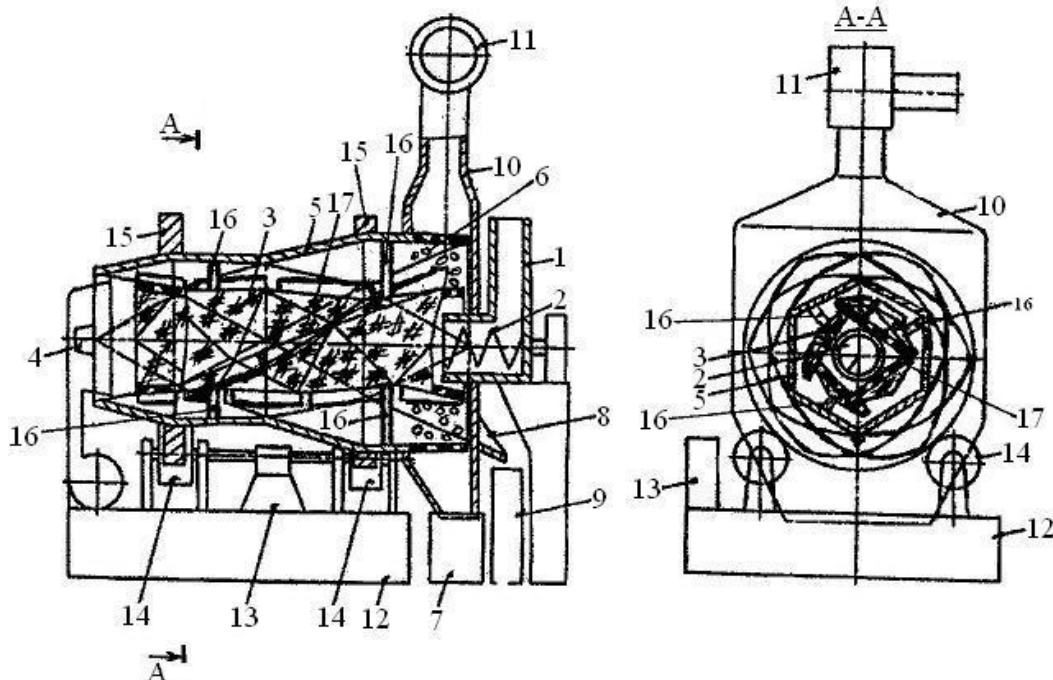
Устройство для сушки куриного помета, вид спереди
